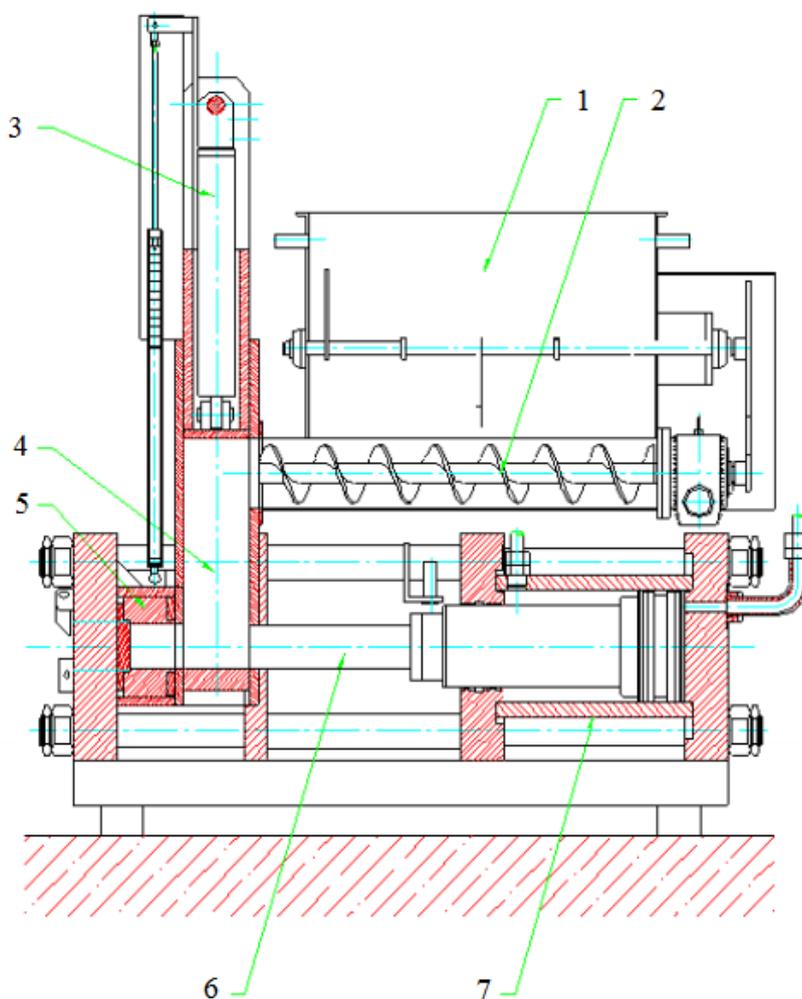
Схема гидравлического пресса: 1 — бункер, 2 — загрузочный шнек, 3 — поршень наполнителя, 4 — камера наполнителя, 5 — пресс-форма, 6 — главный прессующий поршень, 7 — прессующий цилиндр
